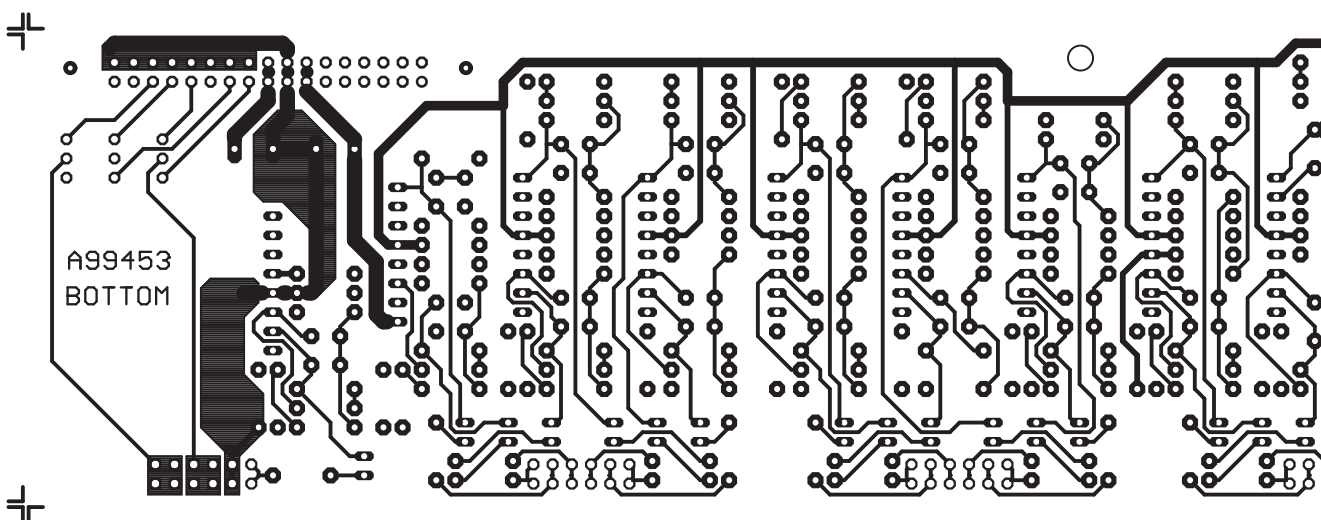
Obrazec desky spojů - vstupů/výstupů grafického equaliseru GE 2031. Strana spojů - BOTTOM
